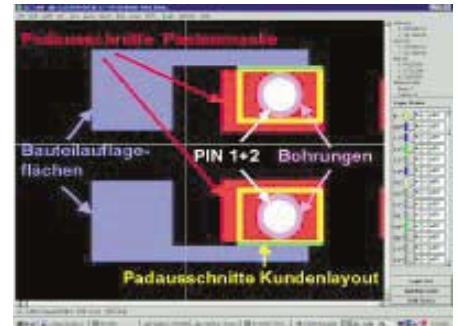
Beispiel für ein CAD-Layout bei Pin in Paste-Lotpads
